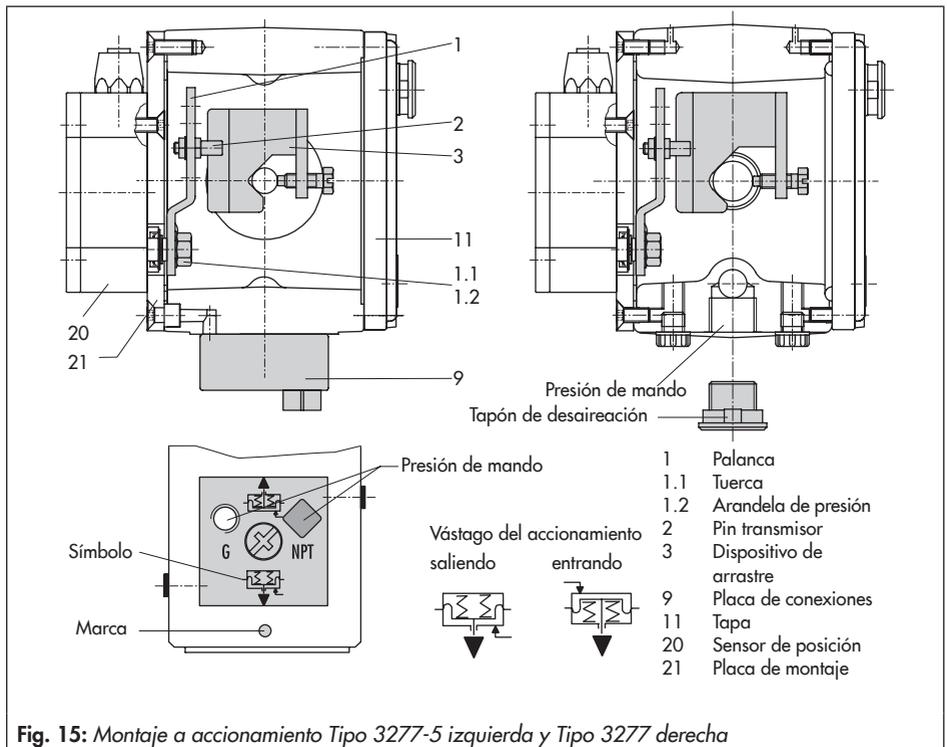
Montaje a accionamiento Tipo 3277-5 izquierda y Tipo 3277 derecha
